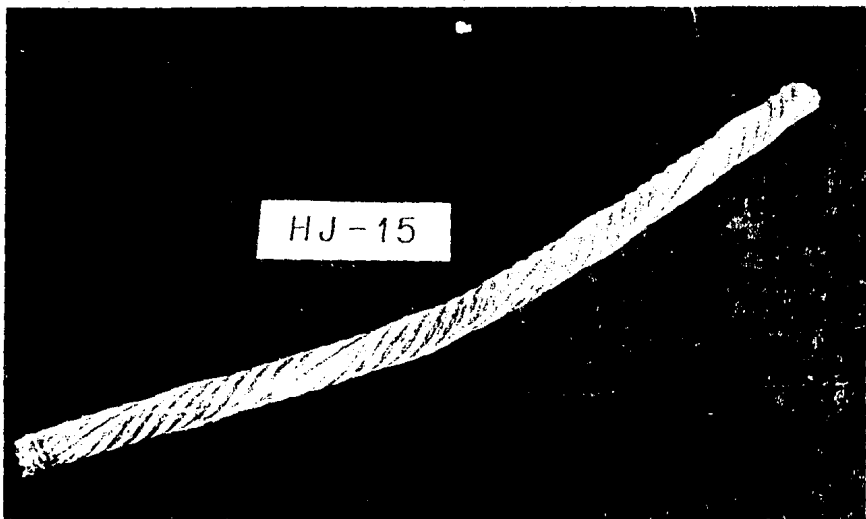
MUESTRA HJ-15, LA SOLDADURA SE ENCUENTRA EN EL EXTREMO INFERIOR IZQUIERDO DE LA FOTOGRAFIA.
